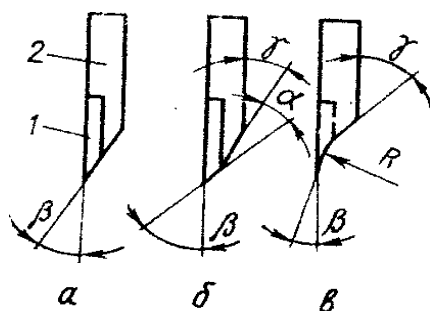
Конструкции режущего ножа и способы его заточки:
